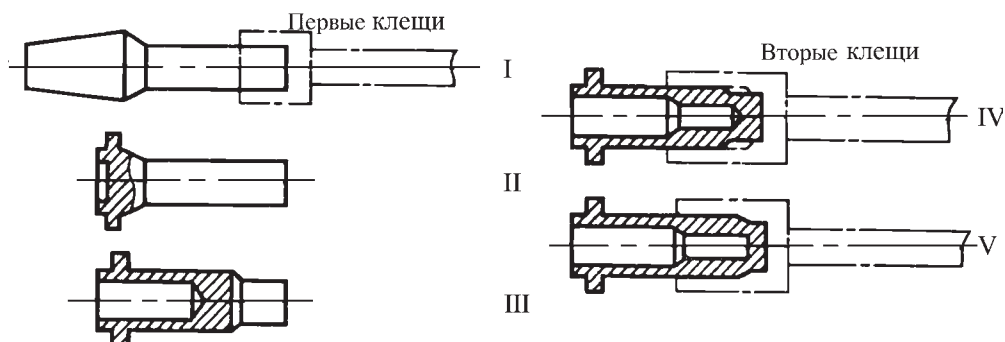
Схема штамповки поковки с глухим отверстием из штучной заготовки:
